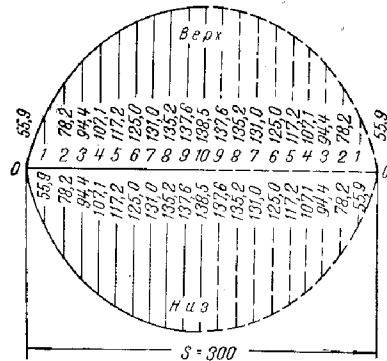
Развертка отверстия в стволе сварного тройника.
